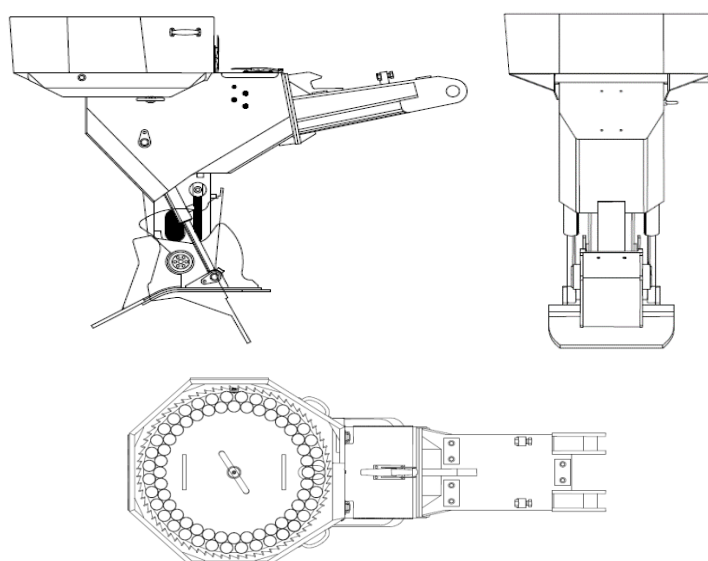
Ilustração do cabeçote Bracke Planter P11.a original com vistas lateral, frontal e superior. Fonte: Bracke Forest (2016)
